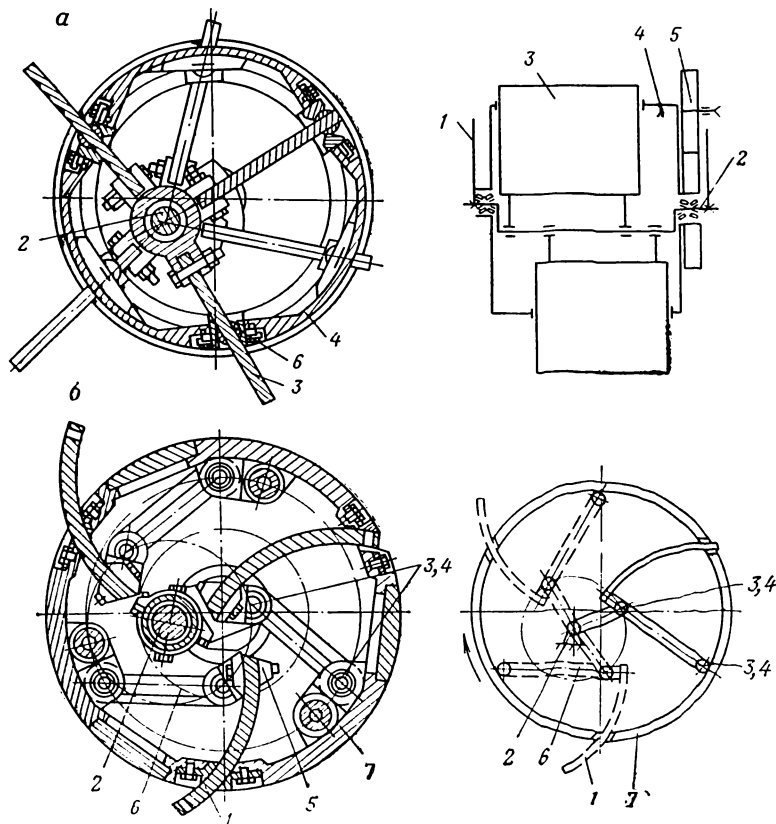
Конструкции и кинематические схемы барабанно-лопастного исполнительного органа:
